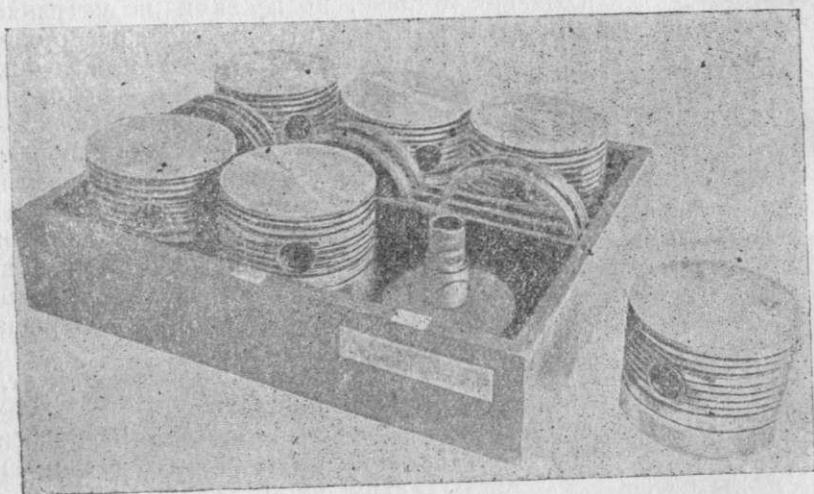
Ящик для поршней, поршневых пальцев и колец
